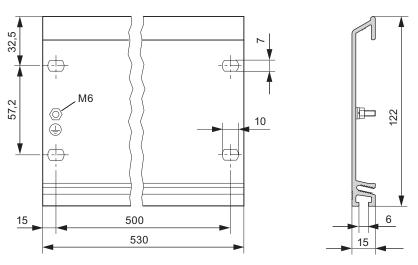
Plan d'encombrement du profilé support de longueur standard 530 mm
